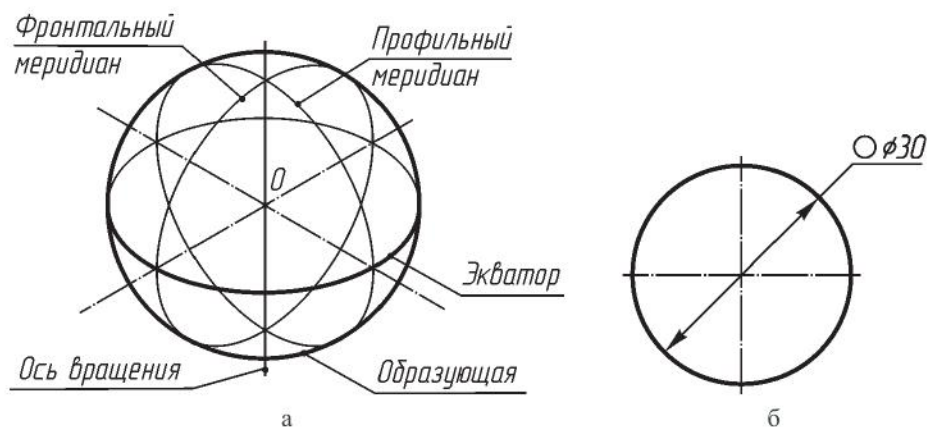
Элементы сферической поверхности и чертеж шара
